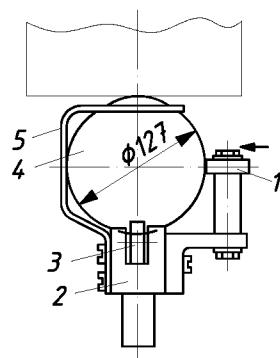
Схема обкатної головки при обкатуванні кулею великого діаметра: 1, 3 - шарикопідшипники; 2 - корпус; 4 - куля; 5 - сепаратор
